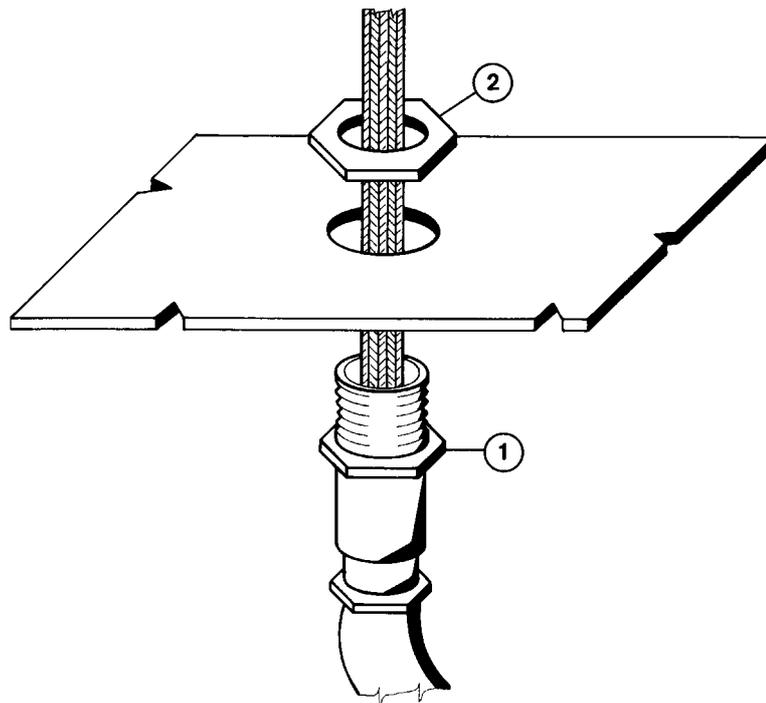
Montaggio passacavi per collegamenti dei circuiti ausiliari
